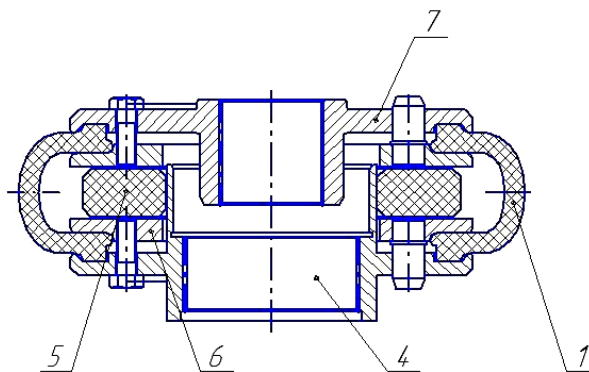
Муфта шинно-зубчатая: 1 - оболочка высокоэластичная; 4 - полумуфта зубчатая; 5 - прокладка; 6 - полукольцо; 7 – полумуфта
